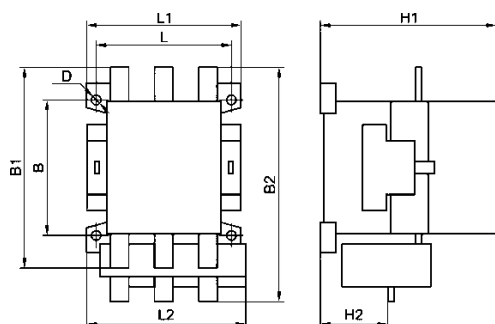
Пускатель неререверсивный ПМА-5000, ПМА-6000, IP00
